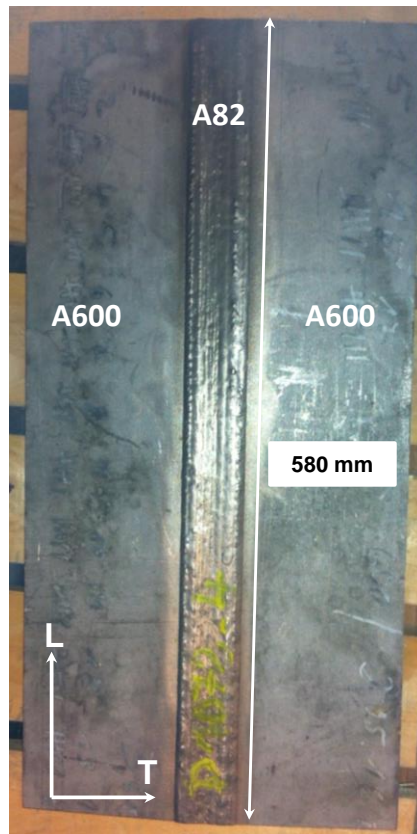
Vue de dessus d’un moule de soudure étudié (soudure repérée D1072)
